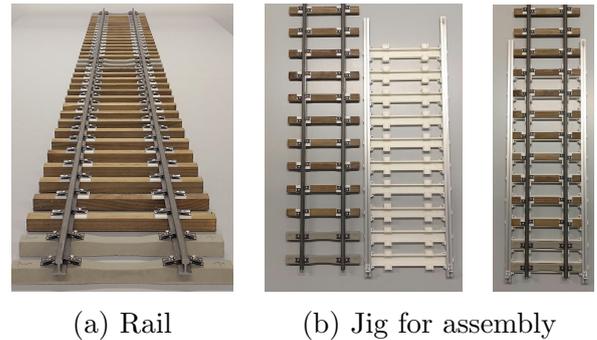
レール (3 [m]) とレール組立用ジグ. Rail unit (approx. 3 [m]-length) with 38 cross-ties and a jig frame for assembly.
